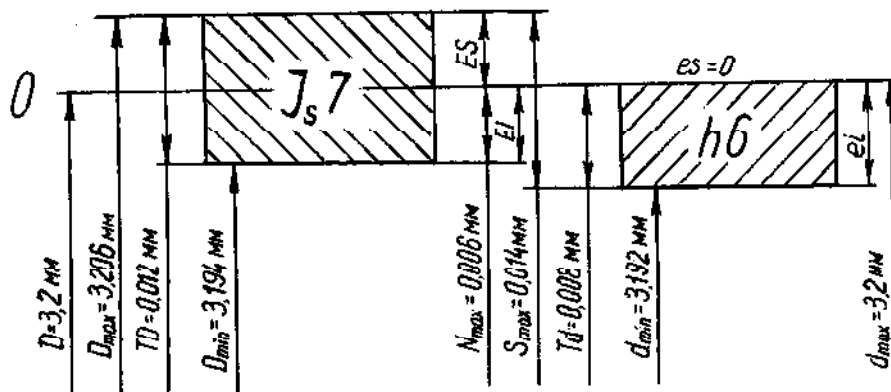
Схема розташування полів допусків отвору та вала
